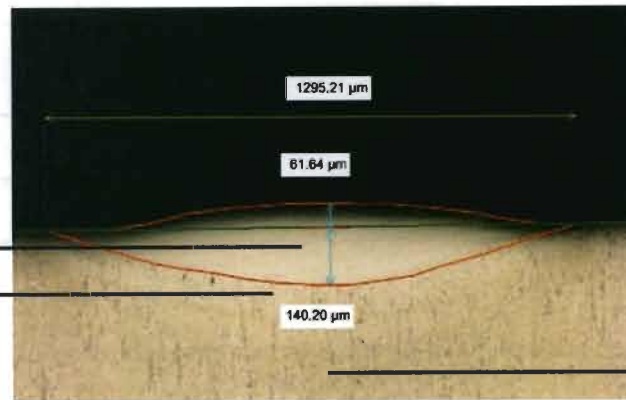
22 Cordón de soldadura #4 visto a 5X
